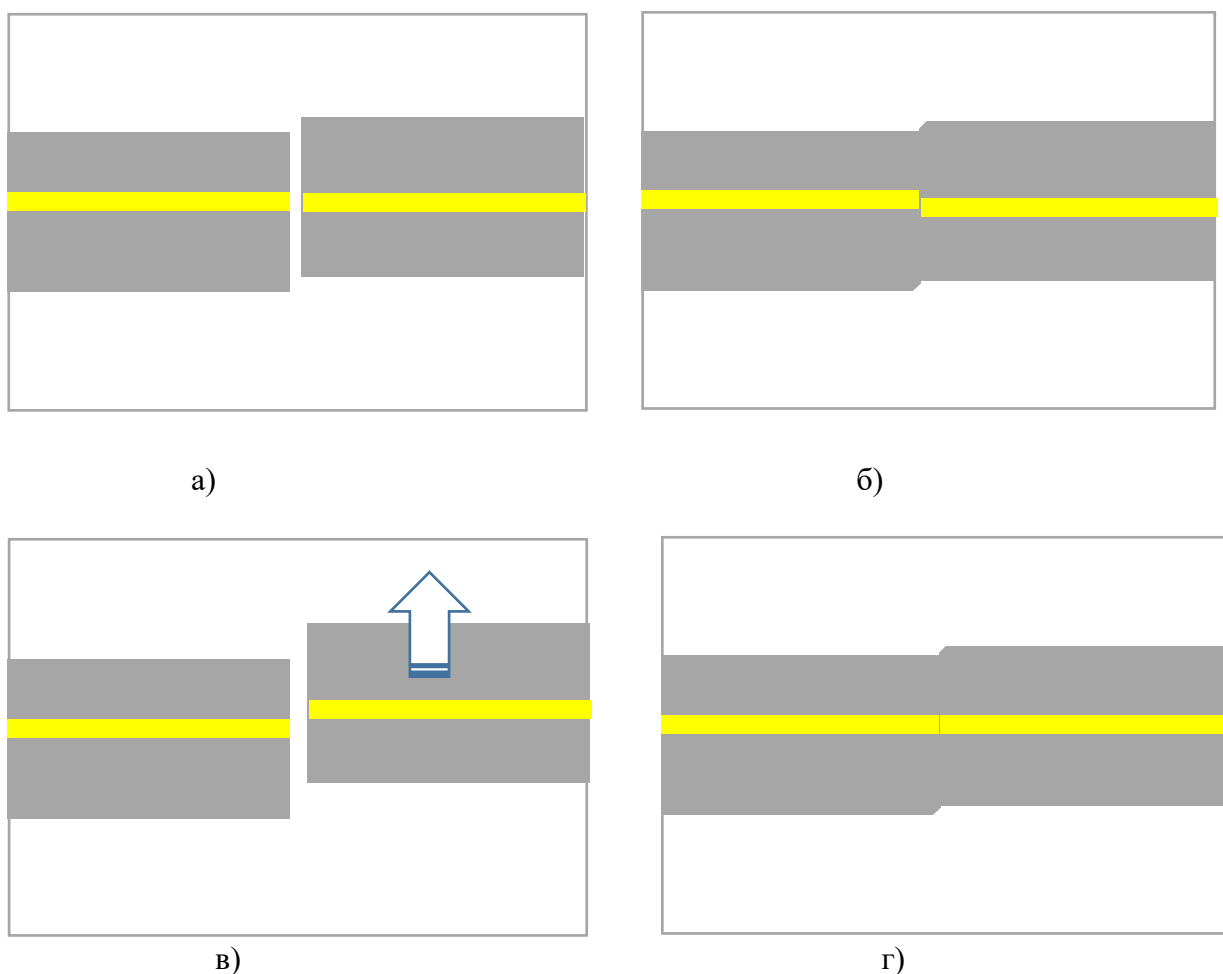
Действие поверхностного натяжения при сварке
